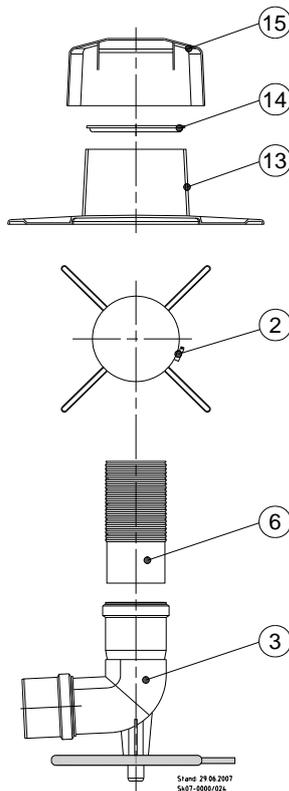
Detail-Zeichnung Befestigung Schachtabdeckung
